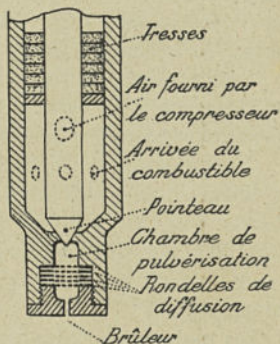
INJECTEUR DU MOTEUR HINDL.
